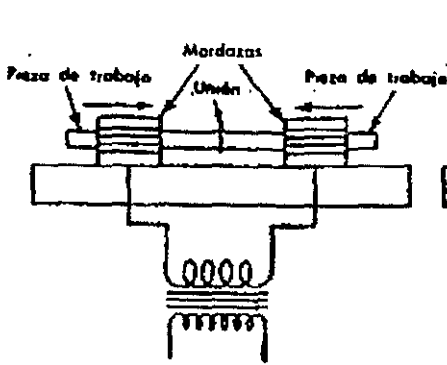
A Diagrama de la soldadura con recalado.
